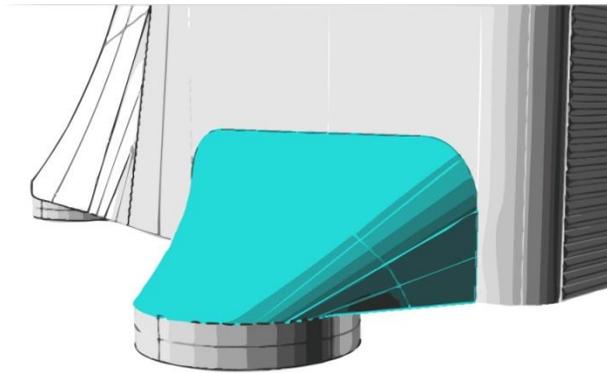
Apoyos para el equipamiento, vista inferior
